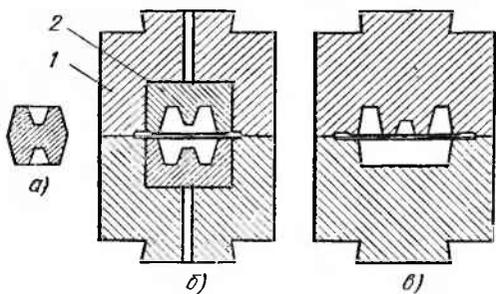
Поковка зубчатого колеса (шестерни) (а), штамп (б) и мастер-штамп (в): 1 — молотовый штамп, 2 — вставка, отштампованная в мастер-штампе
